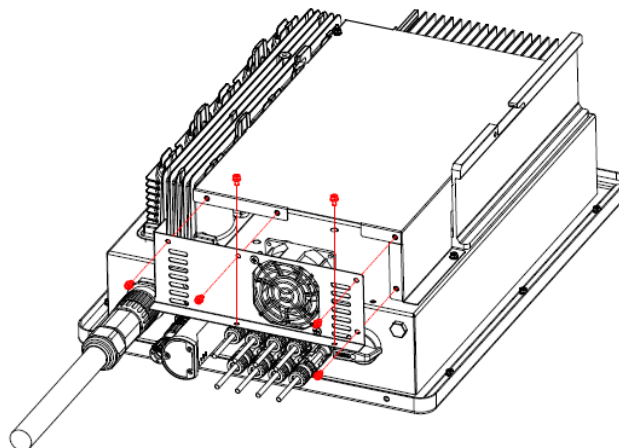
Remova os parafusos de fixação do suporte do ventilador
